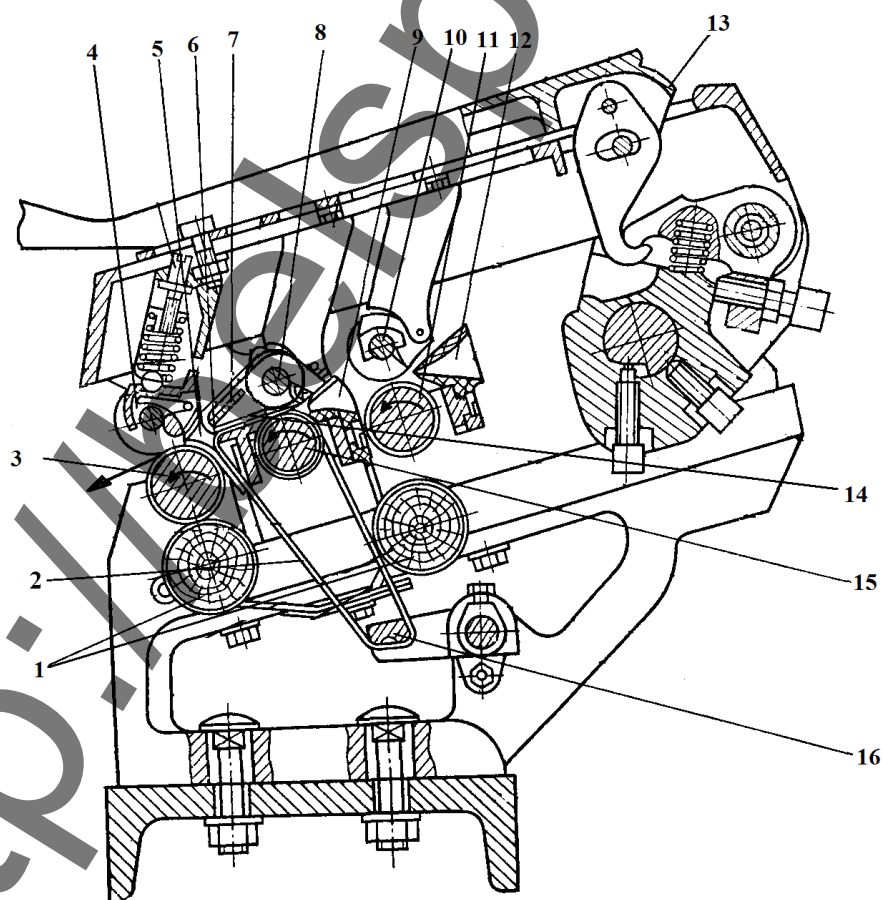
Трехцилиндровый двухремешковый вытяжной прибор
